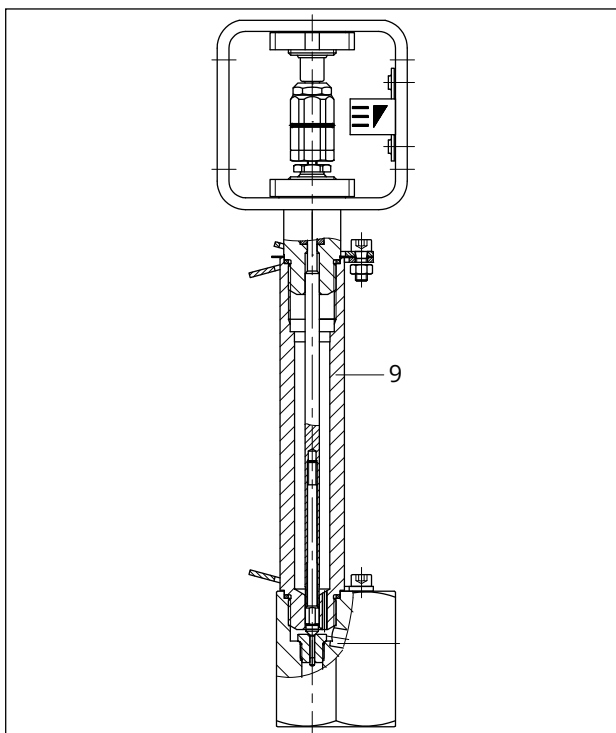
Vanne de régulation type 3510, vanne à passage équerre avec pièce d'isolement
